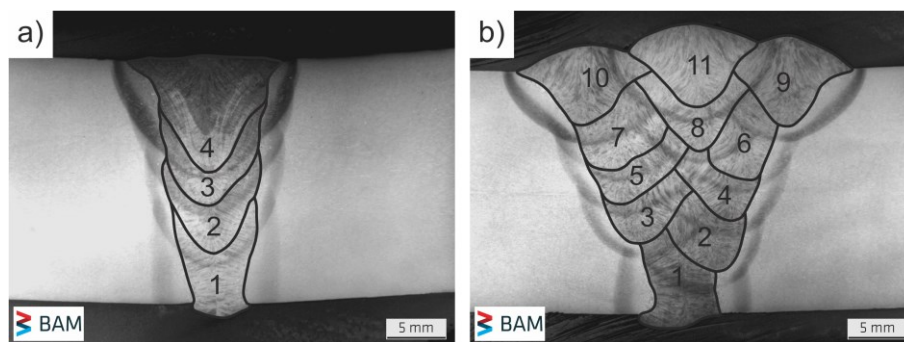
Exemplarische lichtmikroskopische Makroaufnahmen der Mehrlagenschweißungen mit Massivdraht für a) MAG-Mod. 1 mit  $30^\circ$  Nahtöffnungswinkel (4 Schweißraupen) und b) MAG-Konv. mit  $60^\circ$  Nahtöffnungswinkel (11 Schweißraupen)
